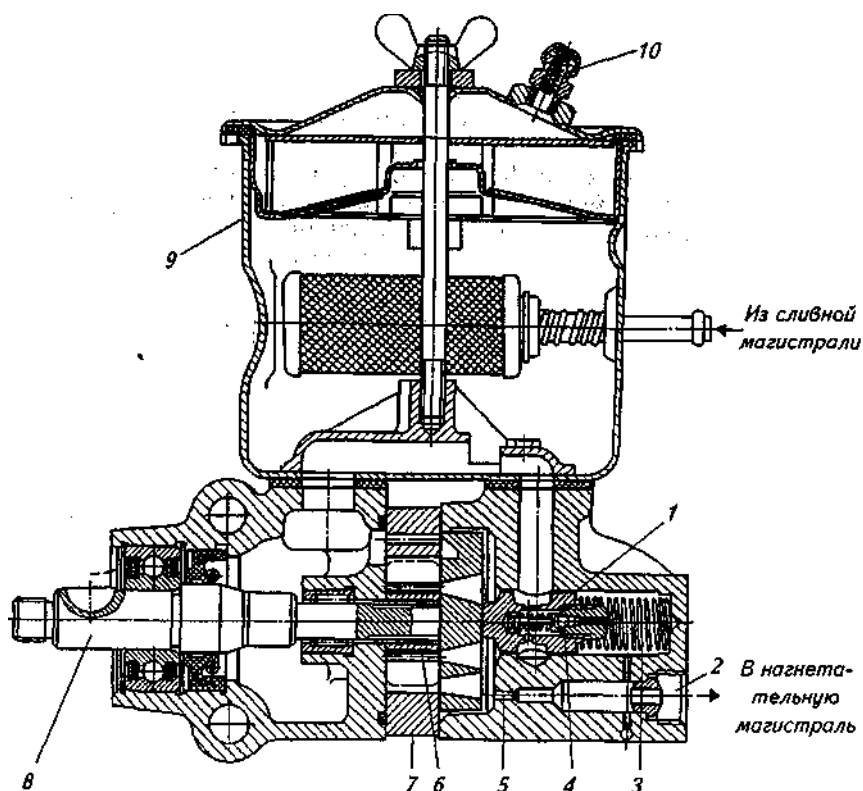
Пластиновый насос гидроусилителя рулевого управления: 1 — клапан расхода; 2— корпус; 3— уравнивающая пружина; 4— предохранительный клапан; 5—жиклер; 6— ротор; 7— статор; 8— приводной вал; 9— бачок; 10— сапун.
